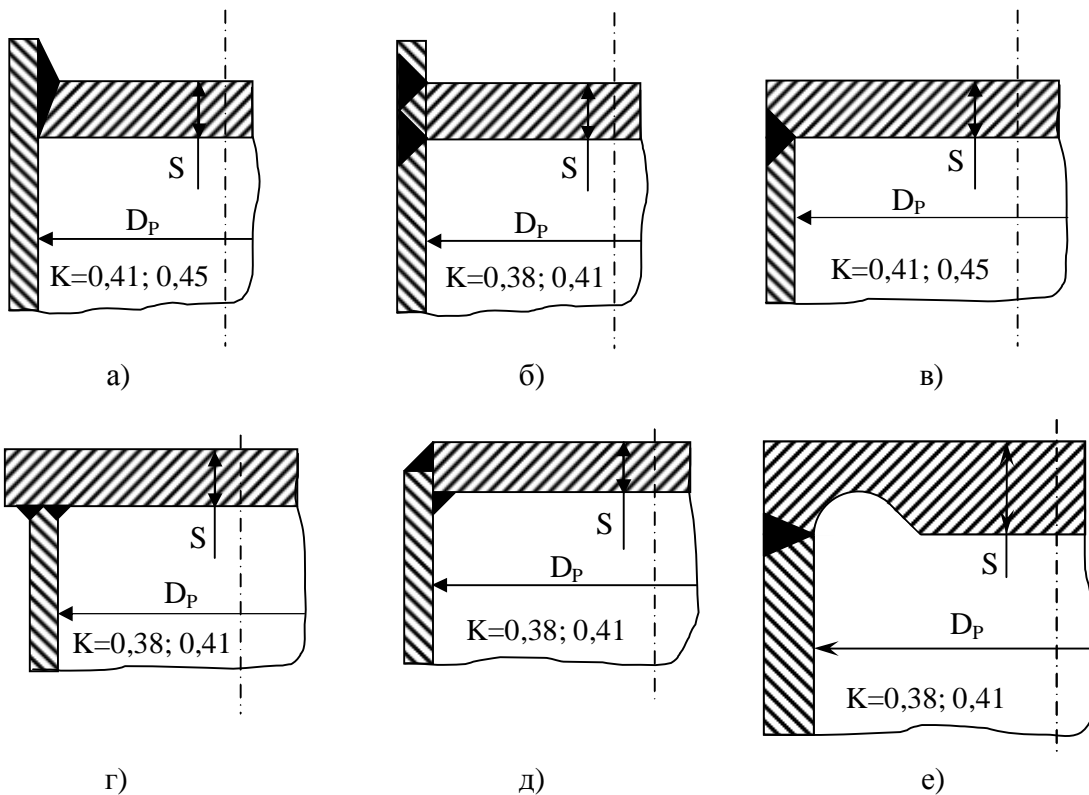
Типовые конструкции сварных плоских днищ
